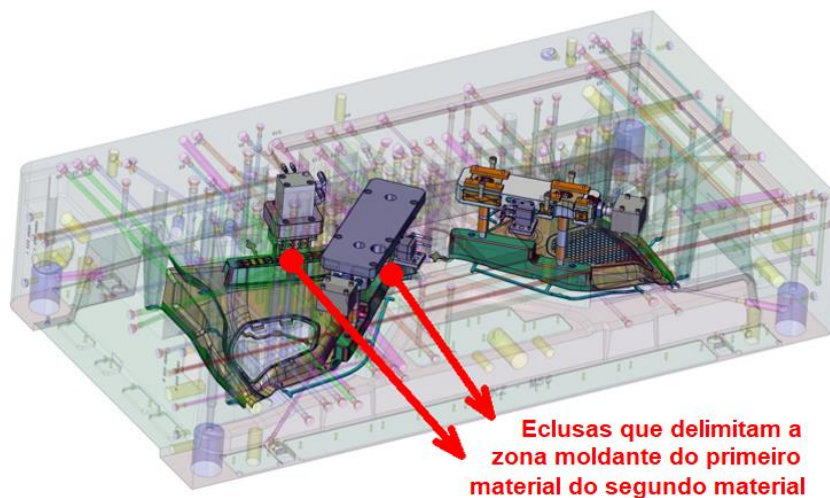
Exemplo de um molde Bi-Material de sistema de eclusas fabricado na SF Moldes.
